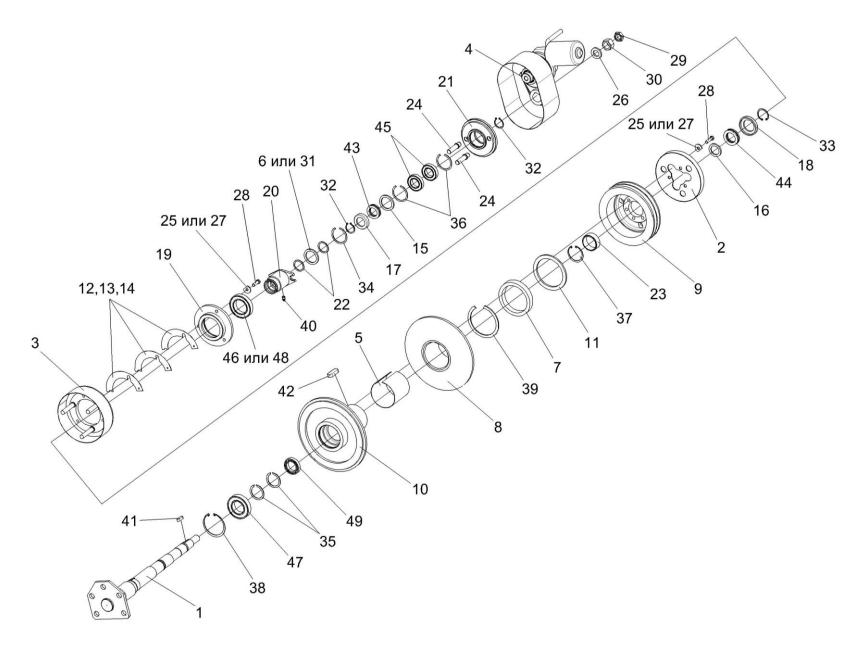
Контрпривод вариатора КЗК-12-0202500А
